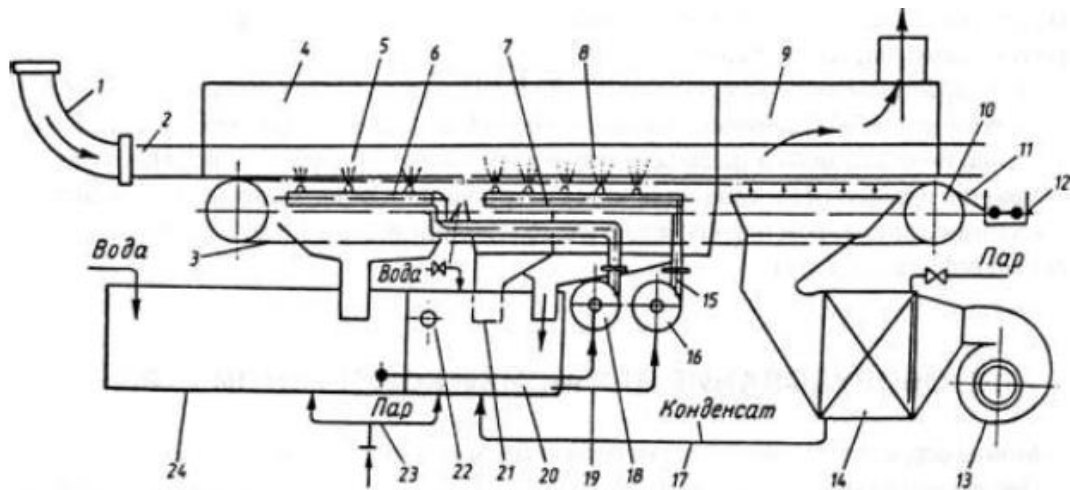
Схема лінійної машини для миття та сушіння металевих банок: 1 - течка; 2 - лоток; 3 - ланцюговий конвеєр; 4,9 - вузли миття та сушіння; 5,8 - форсунки; 6,7 - колектори; 10 - провідна станція конвеєрів; 11 - напрямні; 12 - похилий лоток; 13 - вентилятор; 14 - калорифер; 15 - нагнітальна труба; 16,18 - відцентрові насоси; 17 - труба для відведення конденсату; 19 - всмоктувальна труба; 20,24 - баки для води; 21 - зливна труба; 22 - переливна труба; 23 - паропровід
